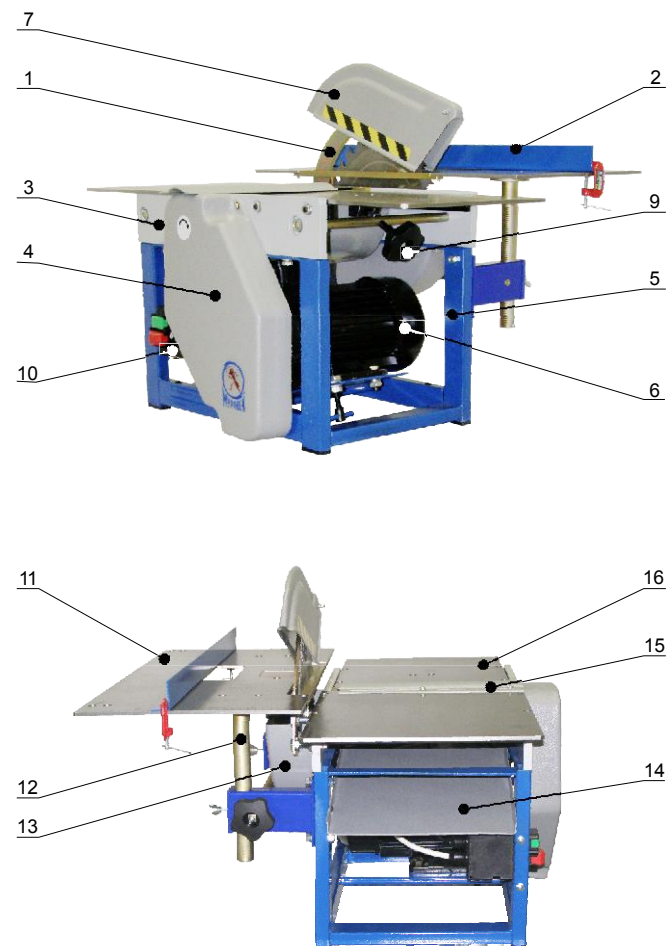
г. Общий вид станка Муравей СД-4-00, СД-4-01
